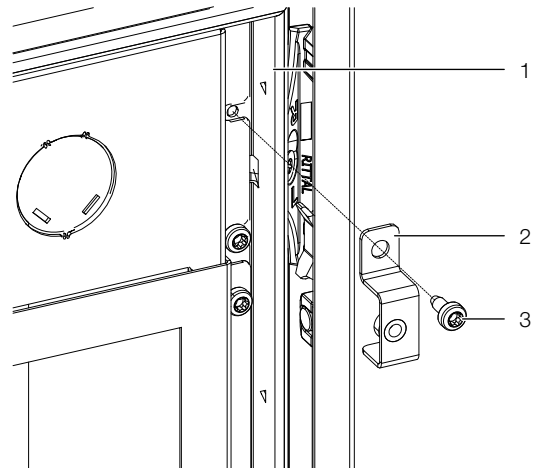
équerres de montage pour la fixation du panneau latéral
